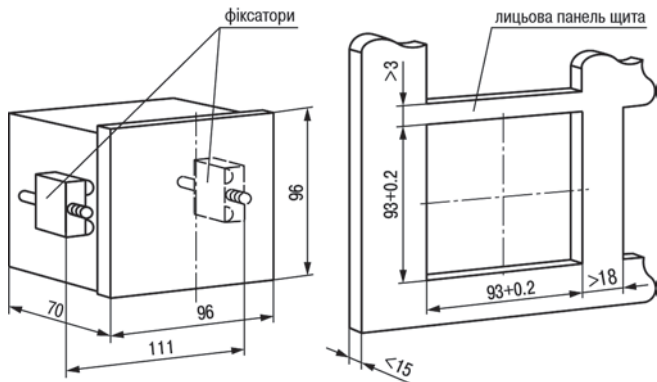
Пристрій щитового кріплення у корпусі типу Щ1
